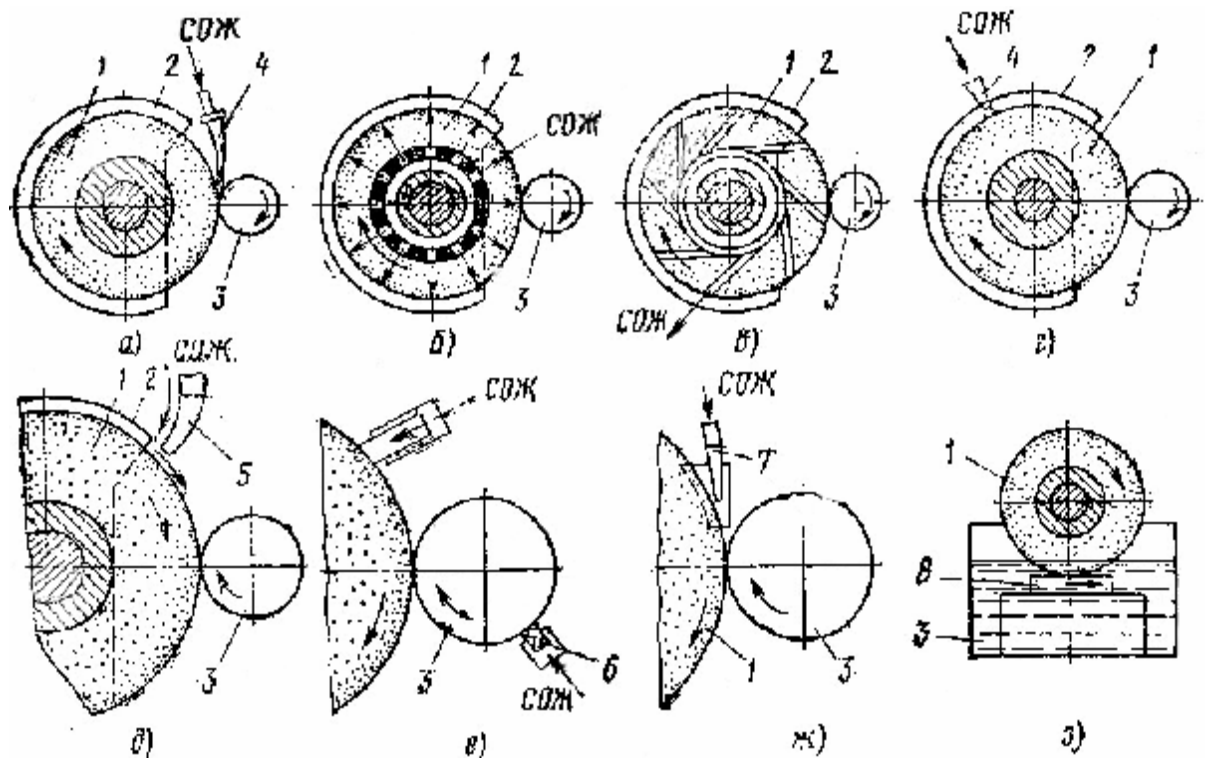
Схемы основных способов подачи СОЖ при шлифовании: 1 – шлифовальный круг; 2 – кожух; 3 – шлифуемая деталь; 4 – сопло; 5 – вибрирующий волновод; 6 – пористый элемент; 7 – насадок; 8 – резервуар.
